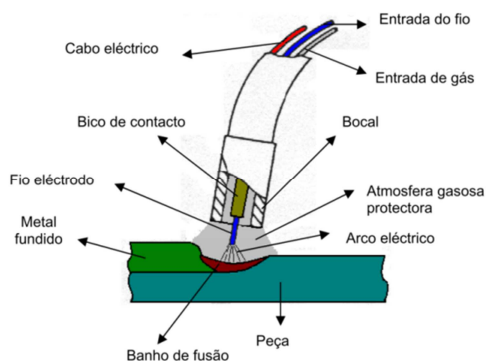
Representação do processo de soldadura MIG/MAG.
